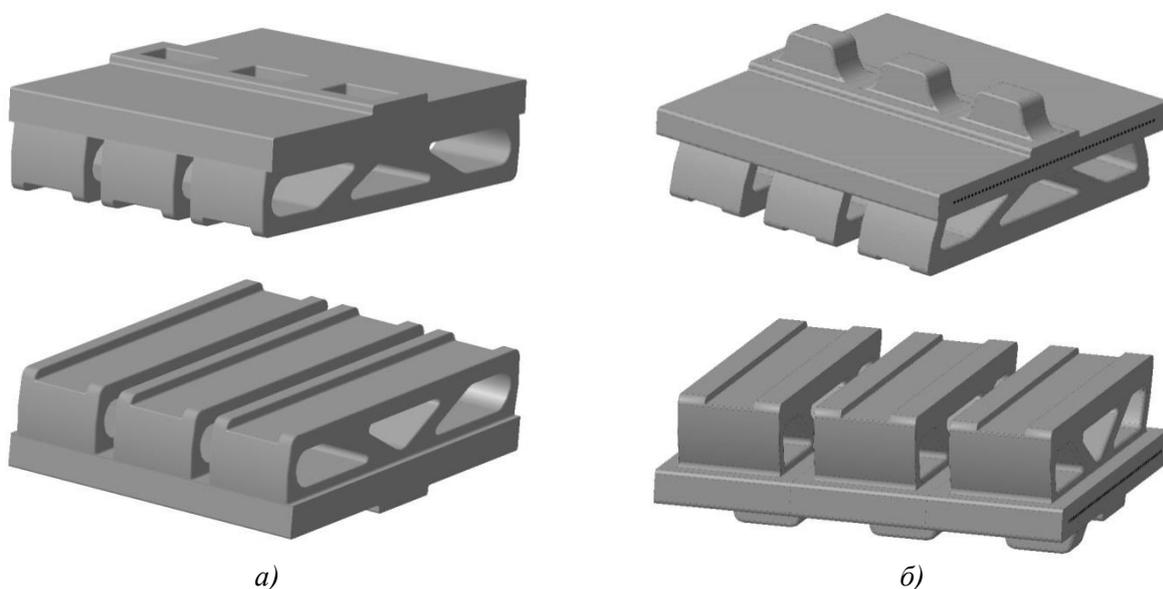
Предлагаемое опорное устройство гусеничного движителя:
